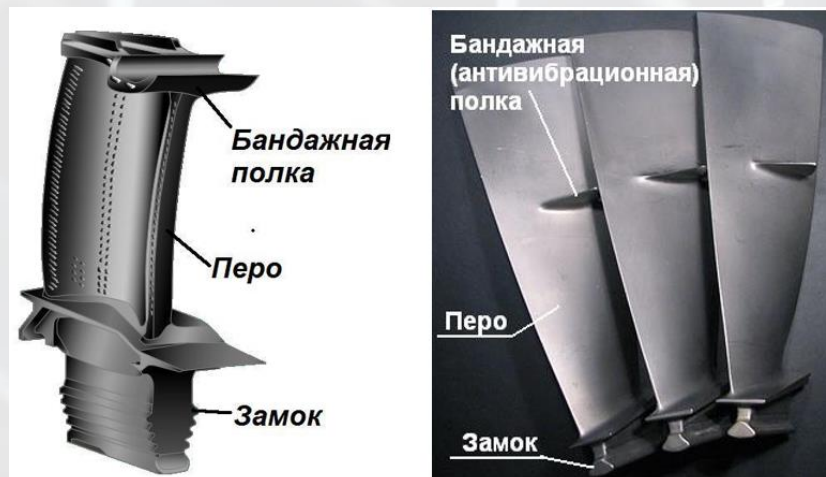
Типовой вид рабочих лопаток осевых турбины (а) и компрессора (б) [7, 8]
